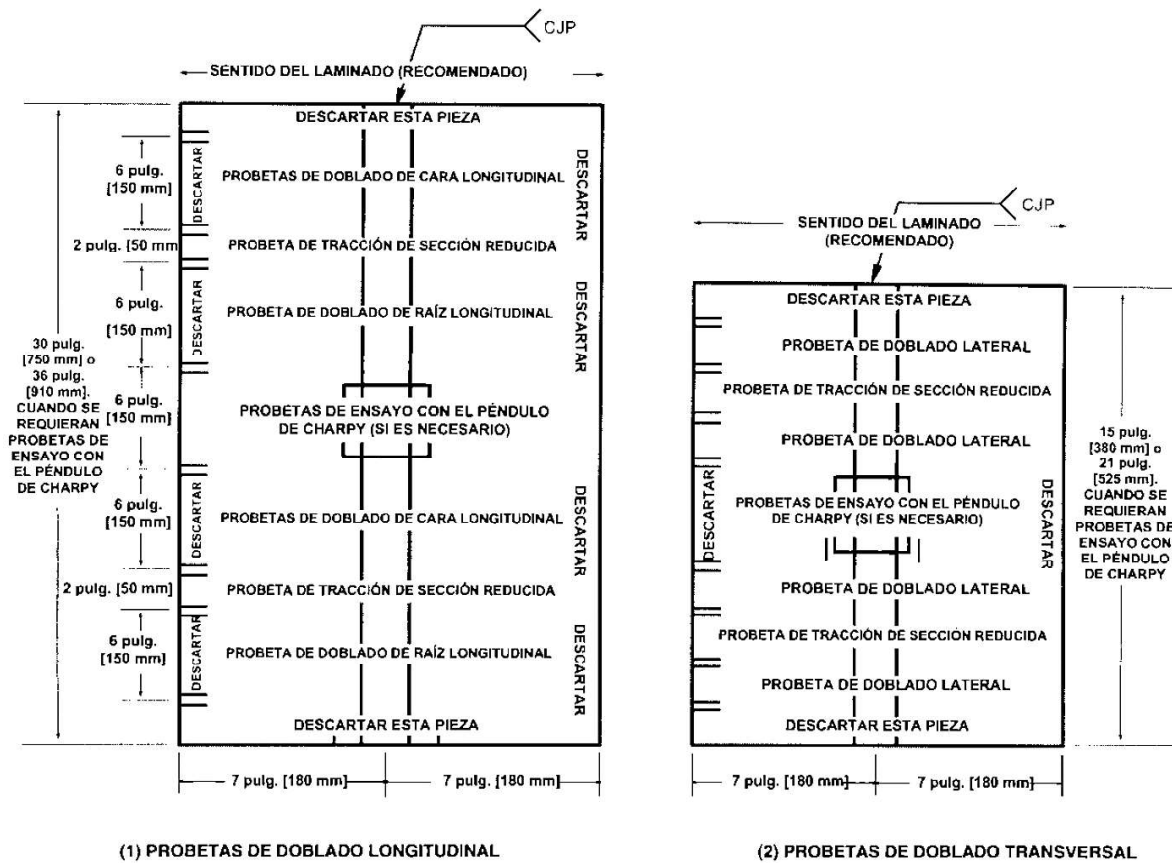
Ubicación de probetas para ensayos mecánicos de la junta soldada para placas mayores a 10 mm.
